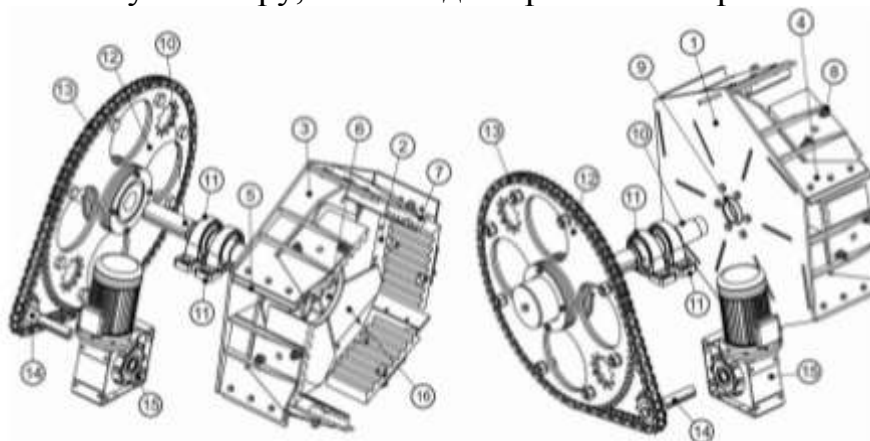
Устройство элеватора ударно-центробежной мельницы «Трибокинетика-3050М»
